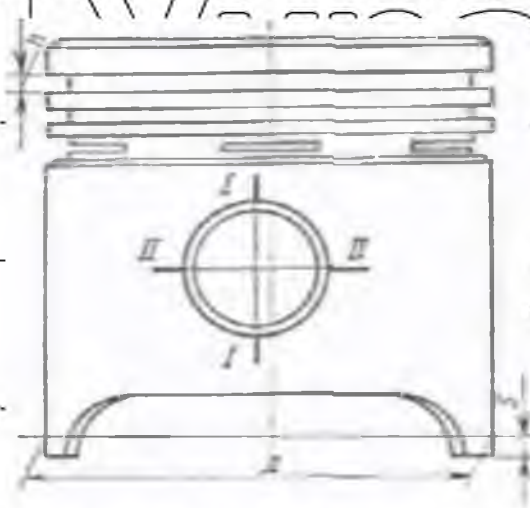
Схема вимірювання зносу робочих поверхонь поршня.
